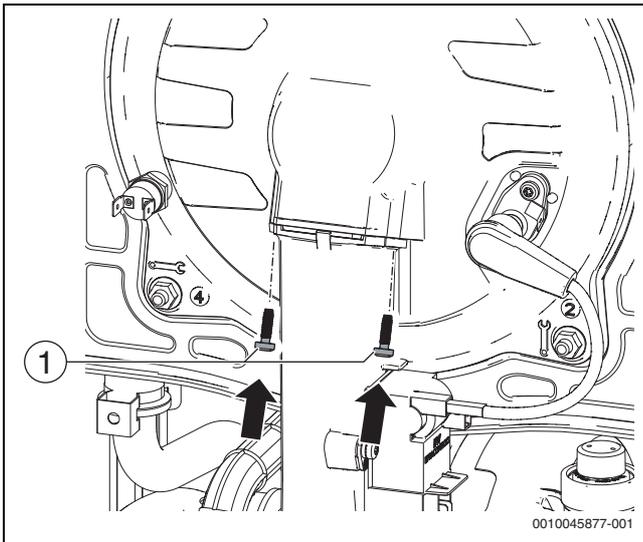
Montaje de los tornillos en la puerta de la cámara de combustión
